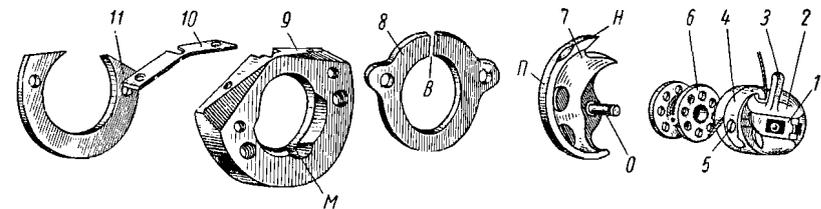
Детали челночного устройства машины 220-го класса ПМЗ
